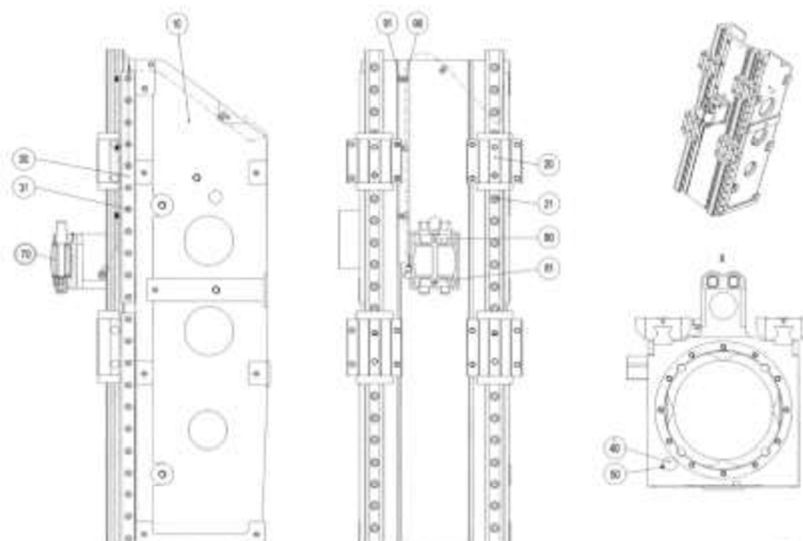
Konstrukční provedení rámu frézky ecoMill50/DMU 50 [32]
